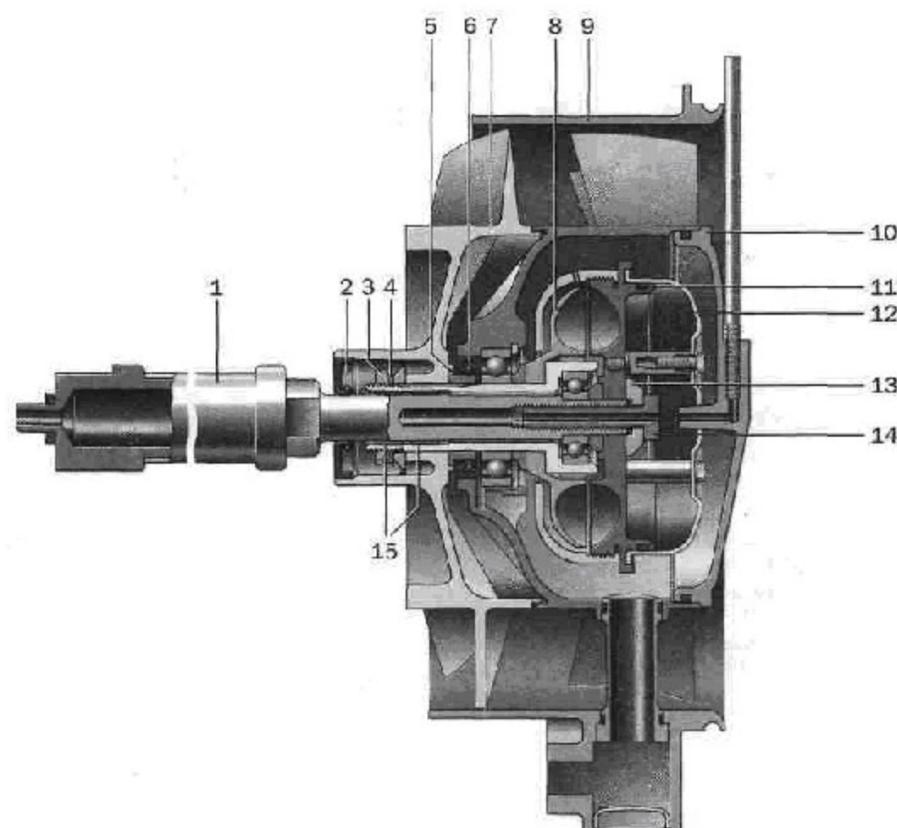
Установка гидравлической муфты в приводе вентилятора: 1 — вал привода вентилятора; 2, 6 — сальники (манжеты); 3 — гайка вала; 4 — стопорная шайба; 5 — втулка сальника; 7 — рабочее колесо; 8 — гидромуфта; 9 — корпус вентилятора; 10 — крышка; 11 — уплотнительное кольцо; 12 — корпус центрифуги; 13 — шайба; 14 — маслопроводный болт; 15 — подшипник скольжения
